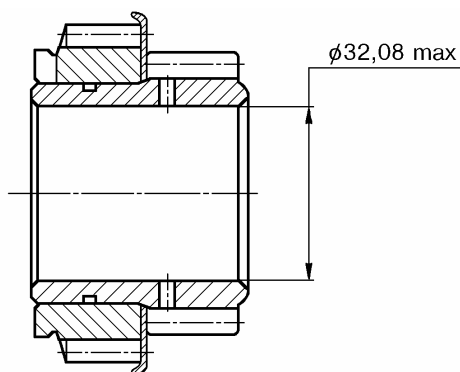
Шестерня V передачи с синхронизатором в сборе – 2107-1701157.
